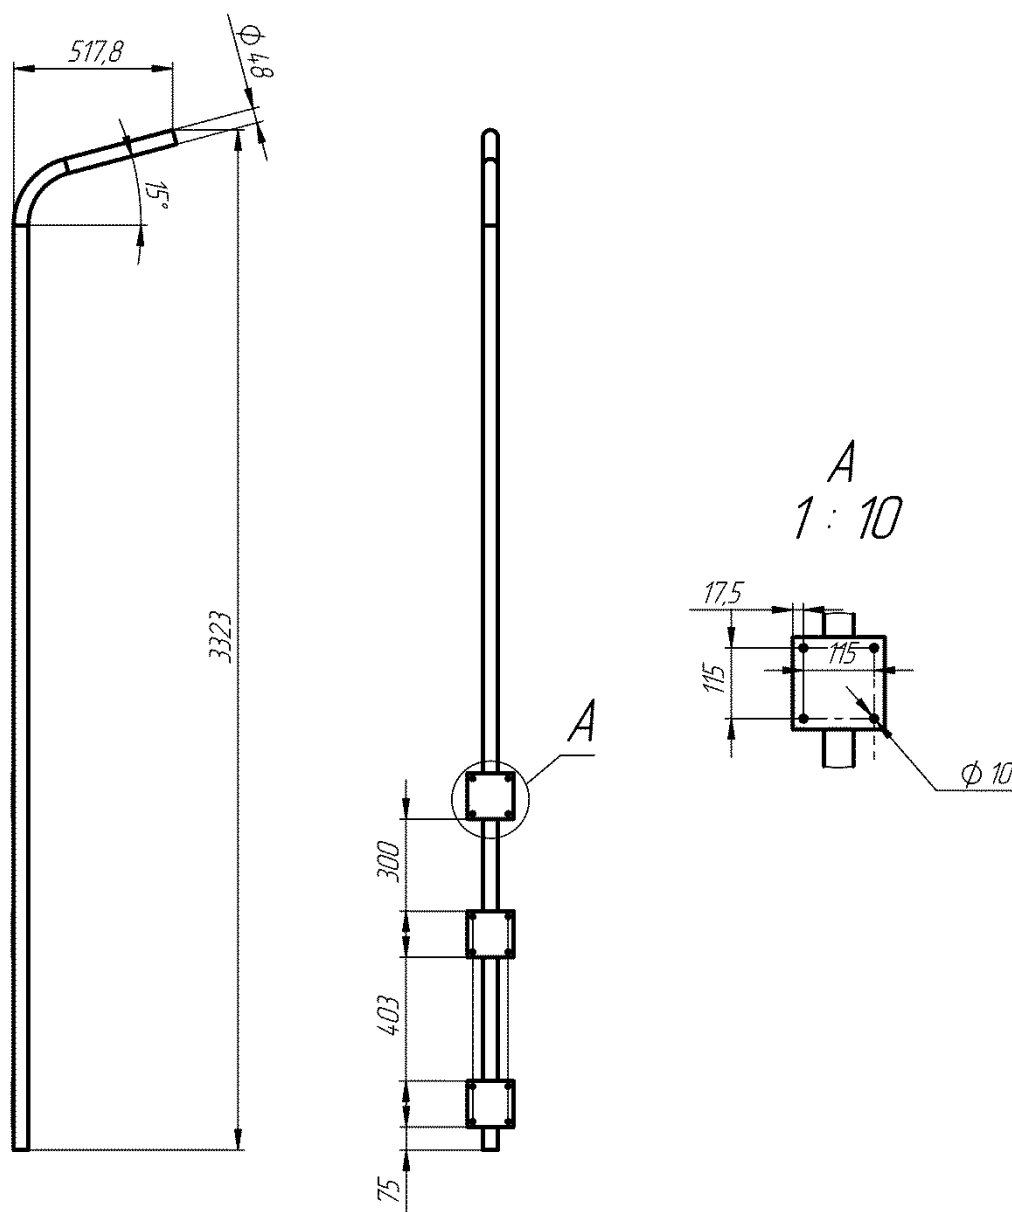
Кронштейн для крепления светильника на бетонное ограждение "Контур-К-8".
